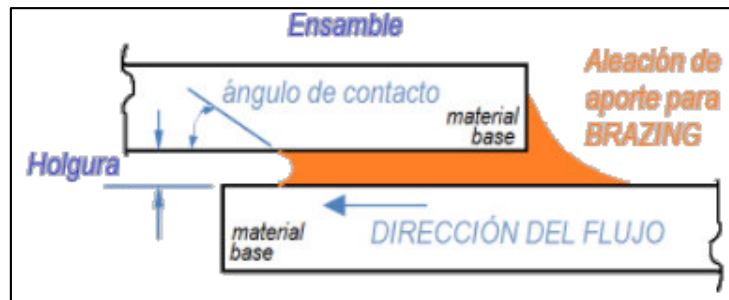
Esquema del proceso de soldadura indirecta.
